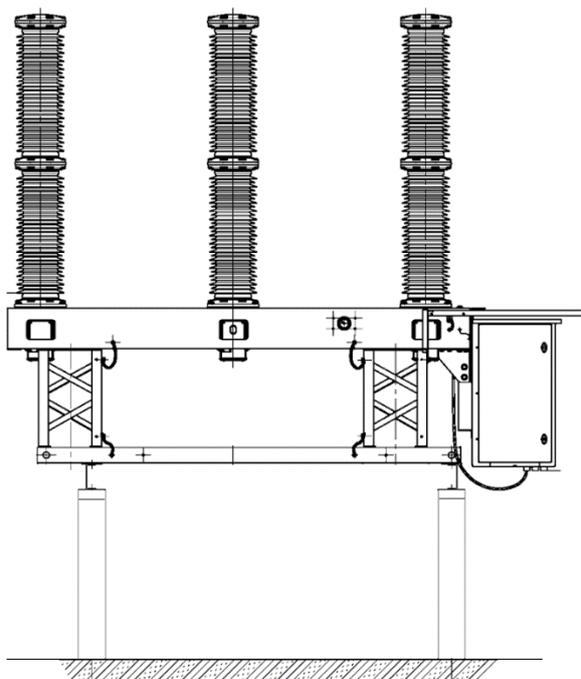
Внешний вид вакуумного выключателя марки ВРС-110
